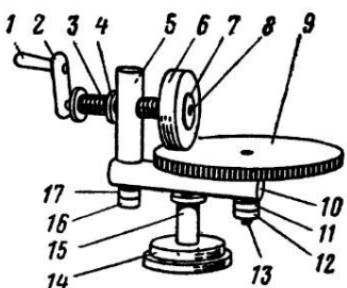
Модель бесступенчатого вариатора скоростей: 1 — ручка; 2 — рычаг ручки; 3 — втулка-регулятор; 4 — контргайка; 5 — кронштейн; 6 — ведущий диск; 7 — металлическая втулка; 8 — вал привода; 9 — ведомый диск; 10 — траверза; 11 — гайка; 12 — контргайка; 13 — ось ведомого диска; 14 — основание; 15 — стойка; 16 — контргайка; 17 — гайка.
